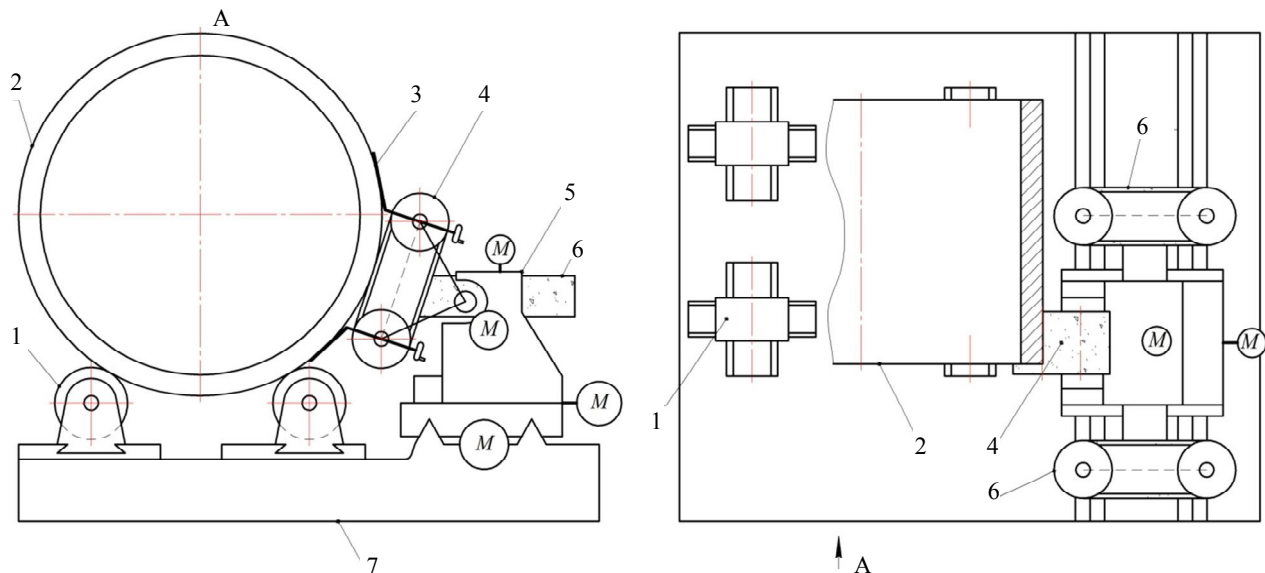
Схема применения станкоробота при шлифовании обечайек и корпусов
